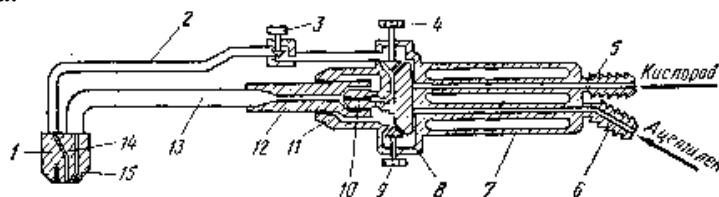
Схема устройства ацетилено-кислородного резака: 1 — головка резака; 2 — трубка режущего кислорода; 3, 4, 9 — вентили; 5, 6 — ниппели для шлангов; 7 — рукоятка; 8 — корпус резака; 10 — инжектор; 11 — накидная гайка; 12 — смесительная камера; 13 — наконечник; 14, 15 — внутренний и наружный мундштуки
